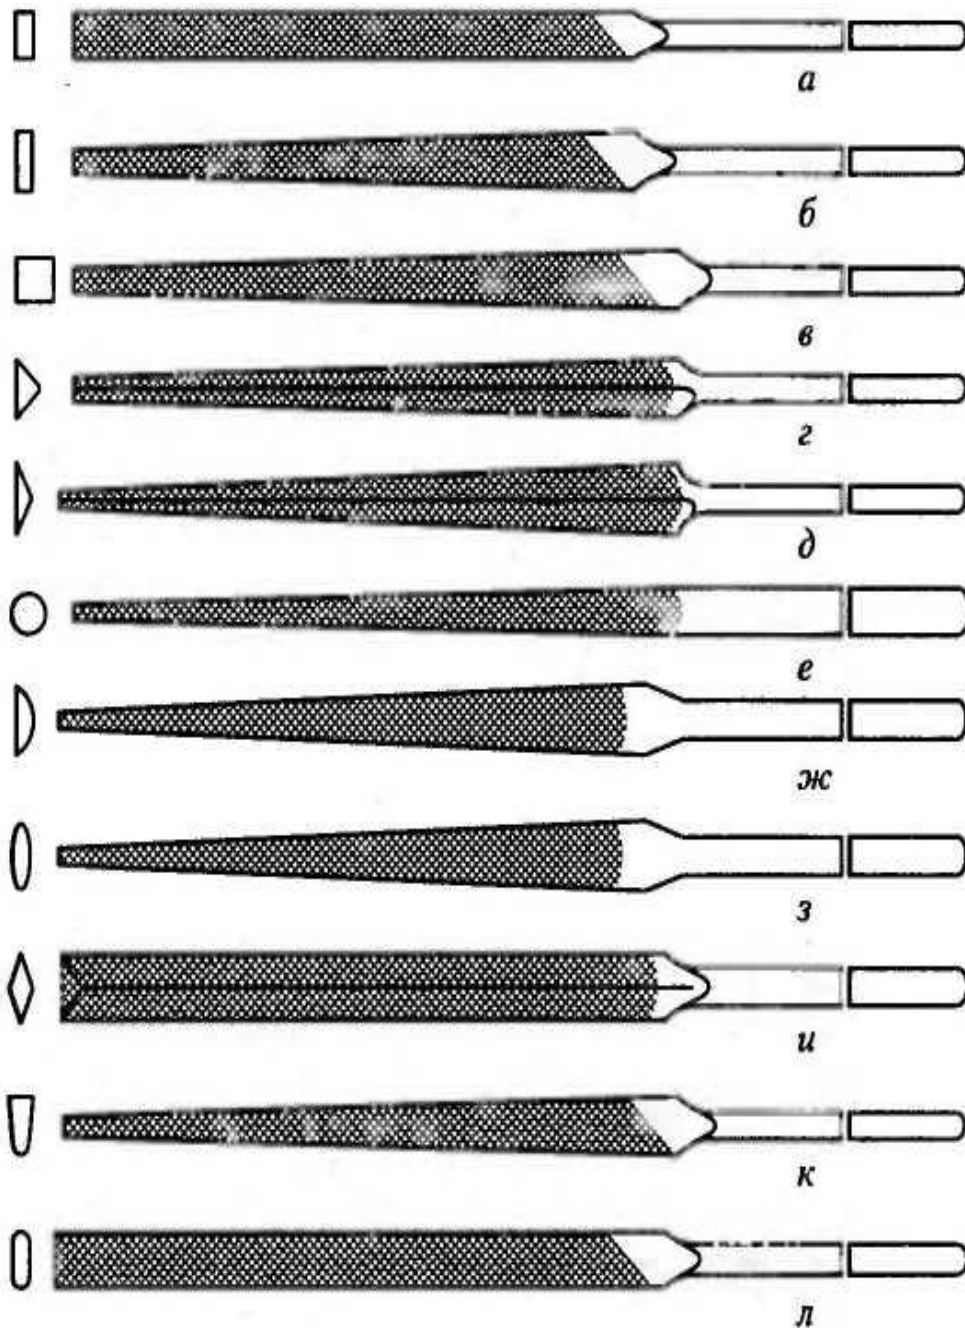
Надфили: а, б - плоские; в — квадратный; г, д — трехгранные; е — круглый; ж — полукруглый; з — оливообразный; и - ромбический; к - трапецеидальный; л - галтельный
